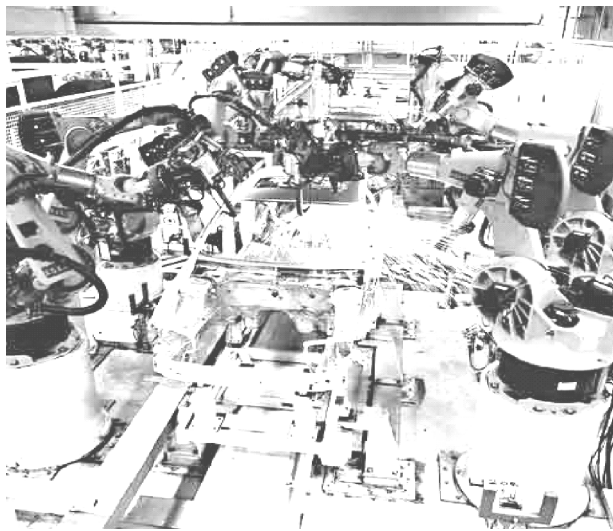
C 型焊钳适合处于较为边缘位置的焊点
